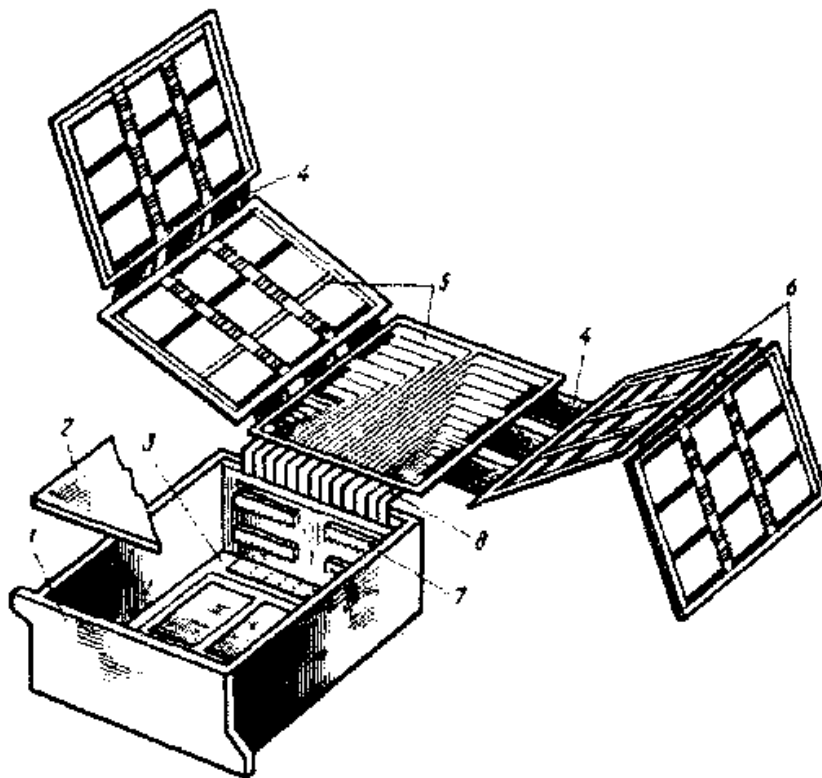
Общий вид блока бортовой ЭВМ: 1 — гермокорпус; 2 — крышка; 5 — плата вторичного источника электропитания; 4 — печатный шлейф; 5 — коммутационная плата на основе полиимидной пленки; 6 — рамка ячейки; 7 — соединитель для внешних связей; 8 — плоский кабель
